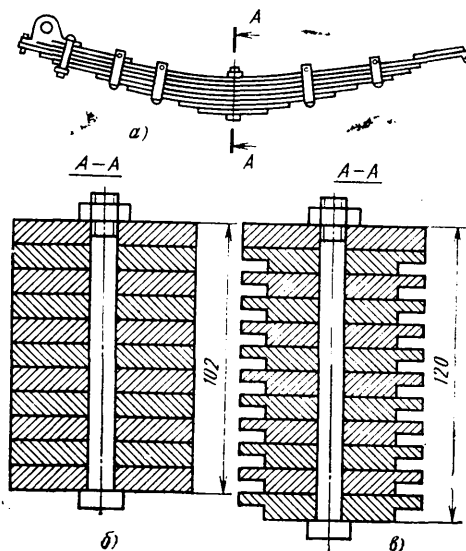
Рессора прицепа ГКБ-817: а — вид рессоры сбоку; б — листы прямоугольного сечения, нагрузка 14 кН; в — листы Т-образного профиля, нагрузка 18 кН
